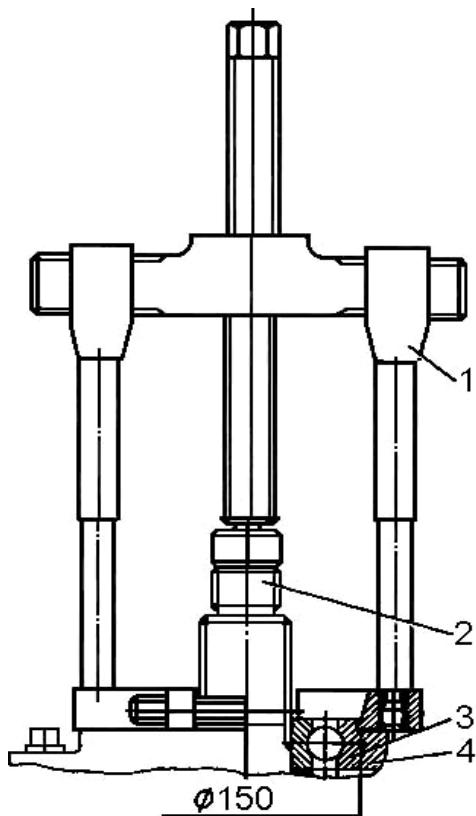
Выпрессовка переднего подшипника первичного вала:
